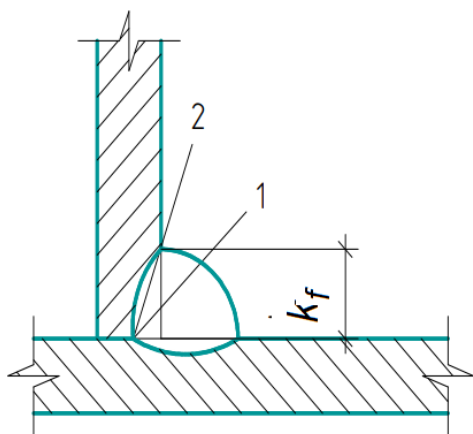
Схема розрахункових перерізів зварного з'єднання з кутовим швом: 1 – переріз по металу шва; 2 – переріз по металу межі сплавлення
